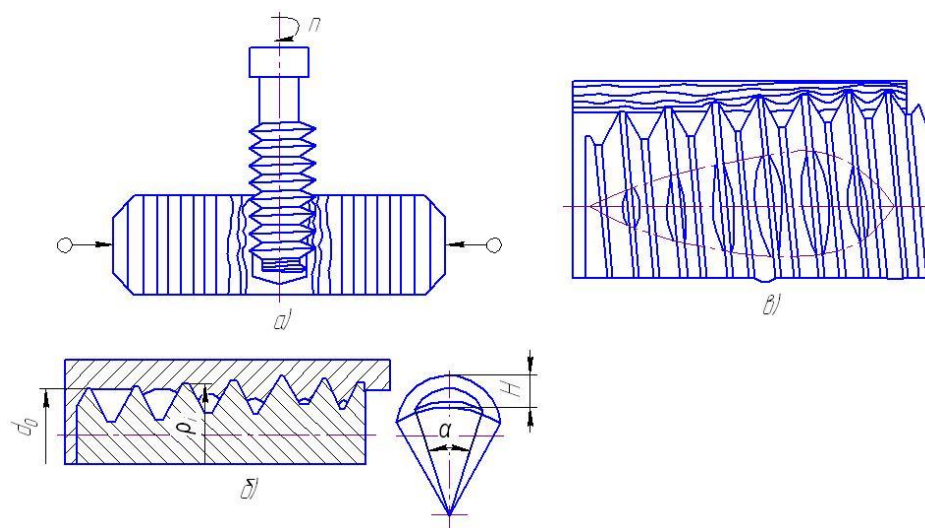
Накатывание резьбы: а) формирование резьбы; б) внедрение зубьев в материал заготовки; в) изменение площадей контакта
